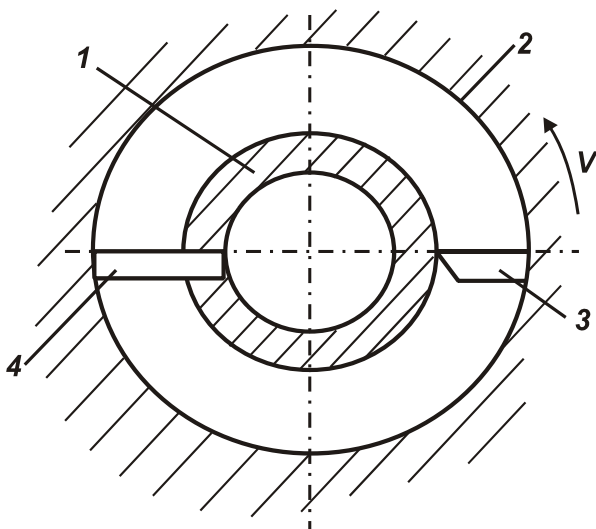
Схема спільної обробки циліндричної й торцевої поверхонь горловини балона
